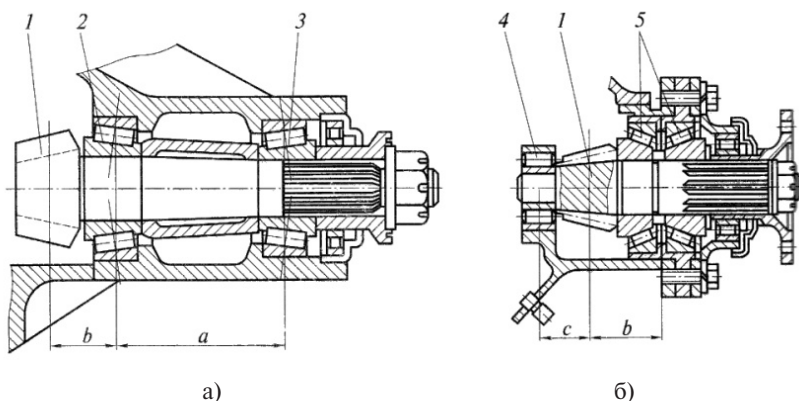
Варианты установки ведущего вала-шестерни конической главной передачи: а — консольное расположение шестерни; б — с дополнительной опорой; 1 — ведущая шестерня; 2, 3, 4, 5 — подшипники; a — расстояние между подшипниками; b , c — плечи приложения окружной силы
